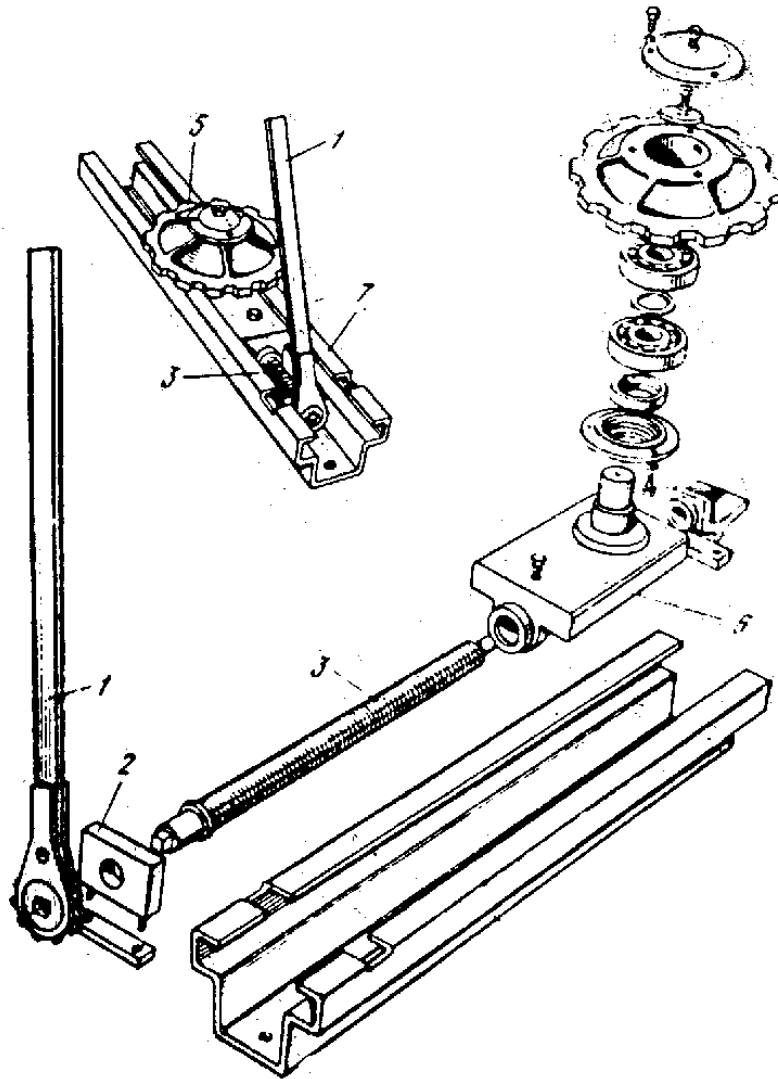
Натяжний пристрій транспортера КСГ- 8 (ТСН –3,0Б): 1 – храпова рукоятка; 2 – підшипник; 3 – гвинт; 4 – вісь повзуна; 5 – поворотна зірочка; 6 – повзун; 7 – рама
